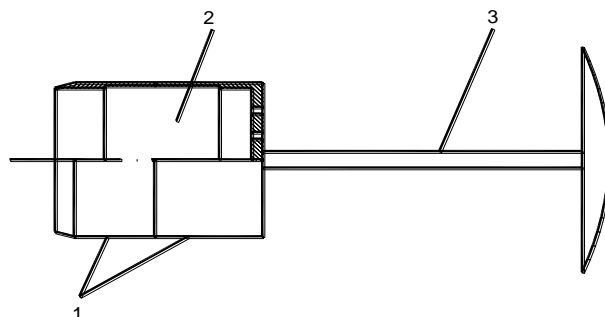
Пробоотборник для отбора образцов почвы со стенок открытых разрезов (1 – составной корпус, 2 – калибровочное пробоотборное кольцо, 3 – толкатель)
